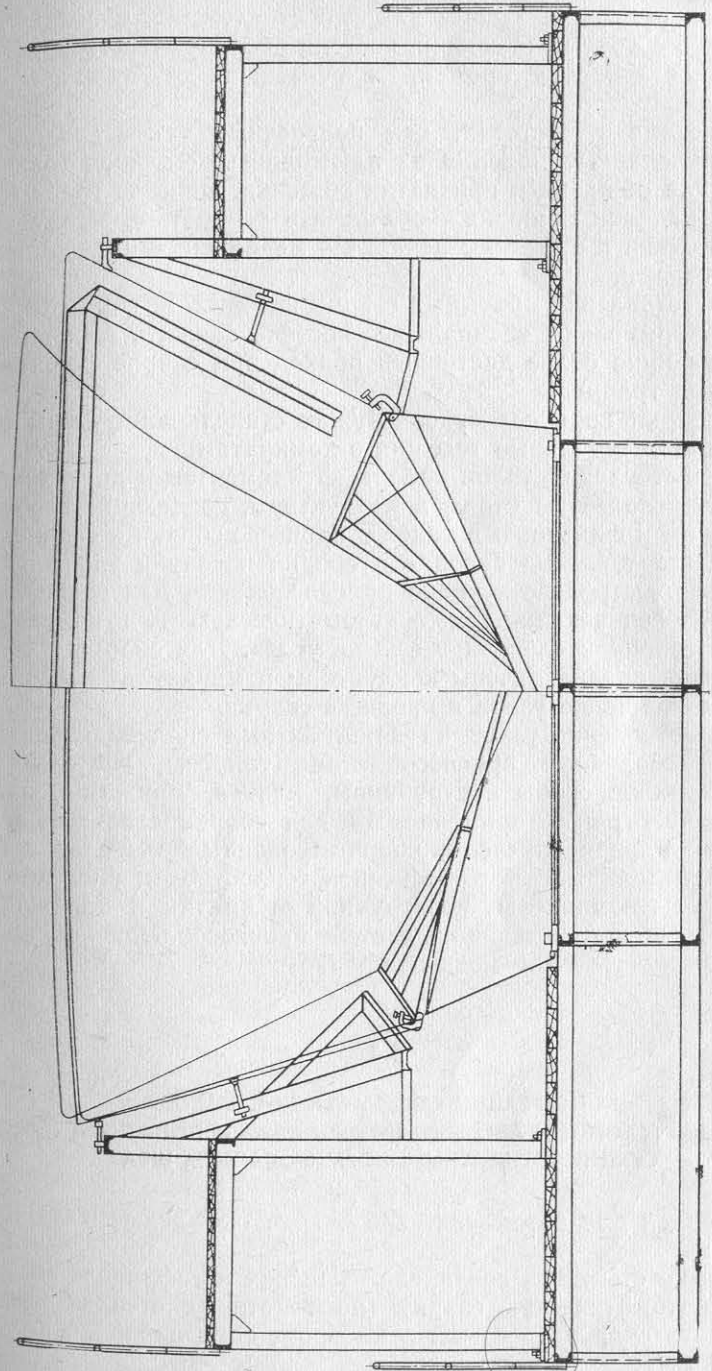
Оснастка для сборки и сварки блоков.
